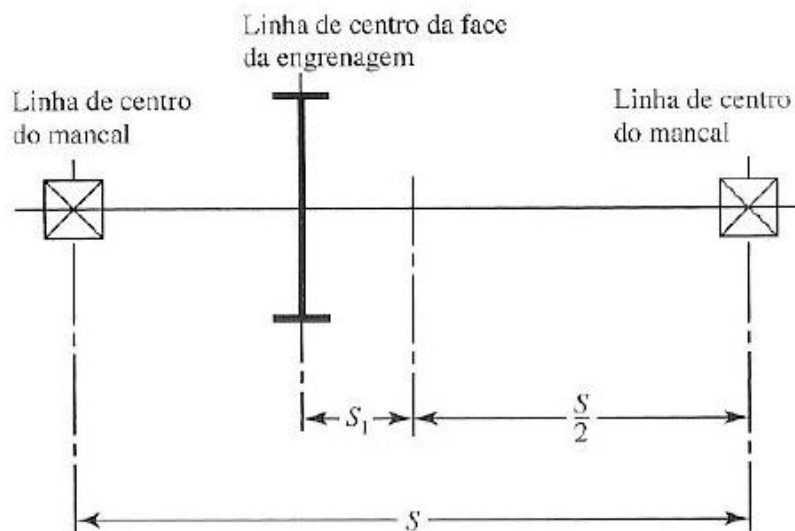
Posicionamento relativo da engrenagem e dos mancais [1].
